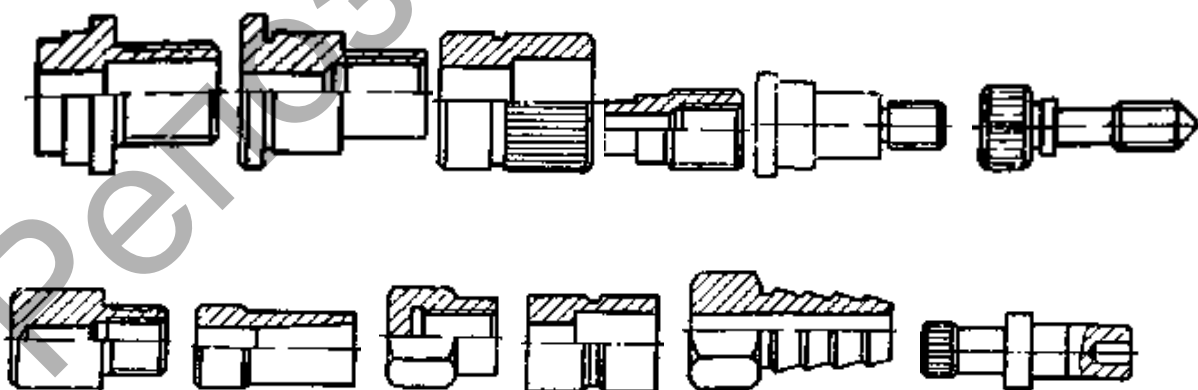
Типовые детали, обрабатываемые на токарно-револьверных автоматах
